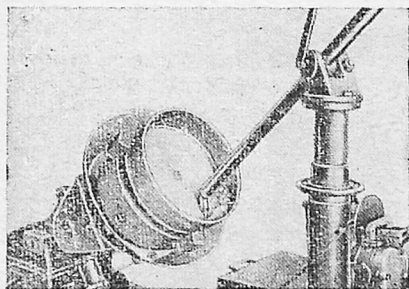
Внутренний вакуумный шов, наложенный под слоем флюса на сварочном станке.
